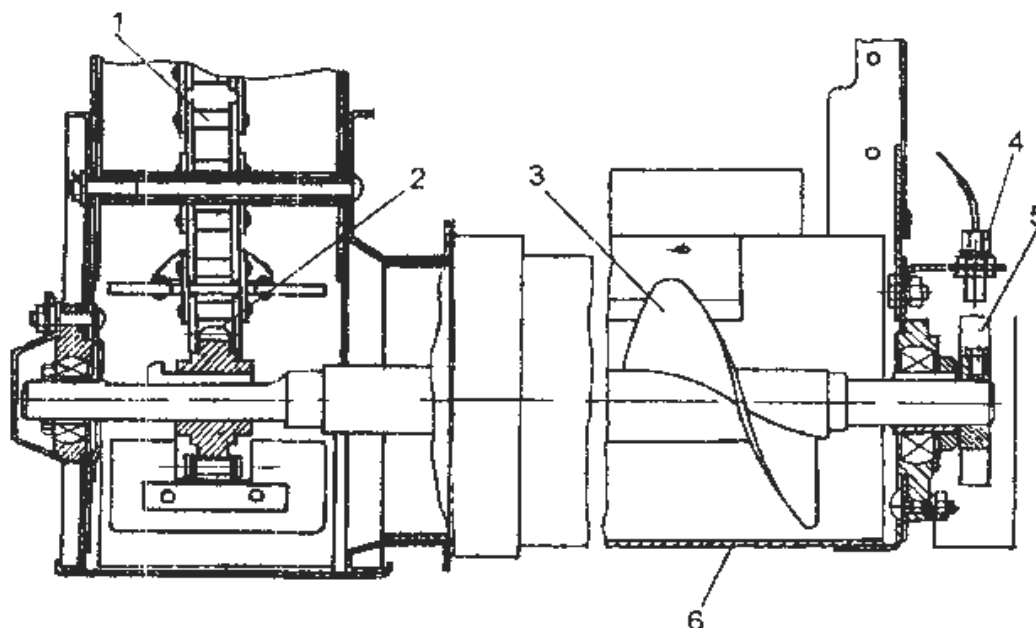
Шнек зерновой: 1 – цепь элеватора; 2 – звездочка; 3 – шнек; 4 – индуктивный датчик; 5 – формироватор; 6 – кожух
